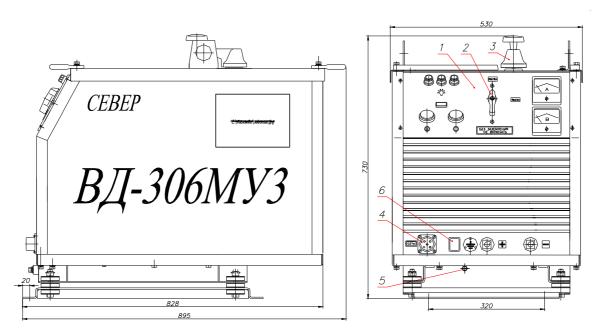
А — Общий вид выпрямителя сварочного ВД-306МУЗ "Север" на платформе
